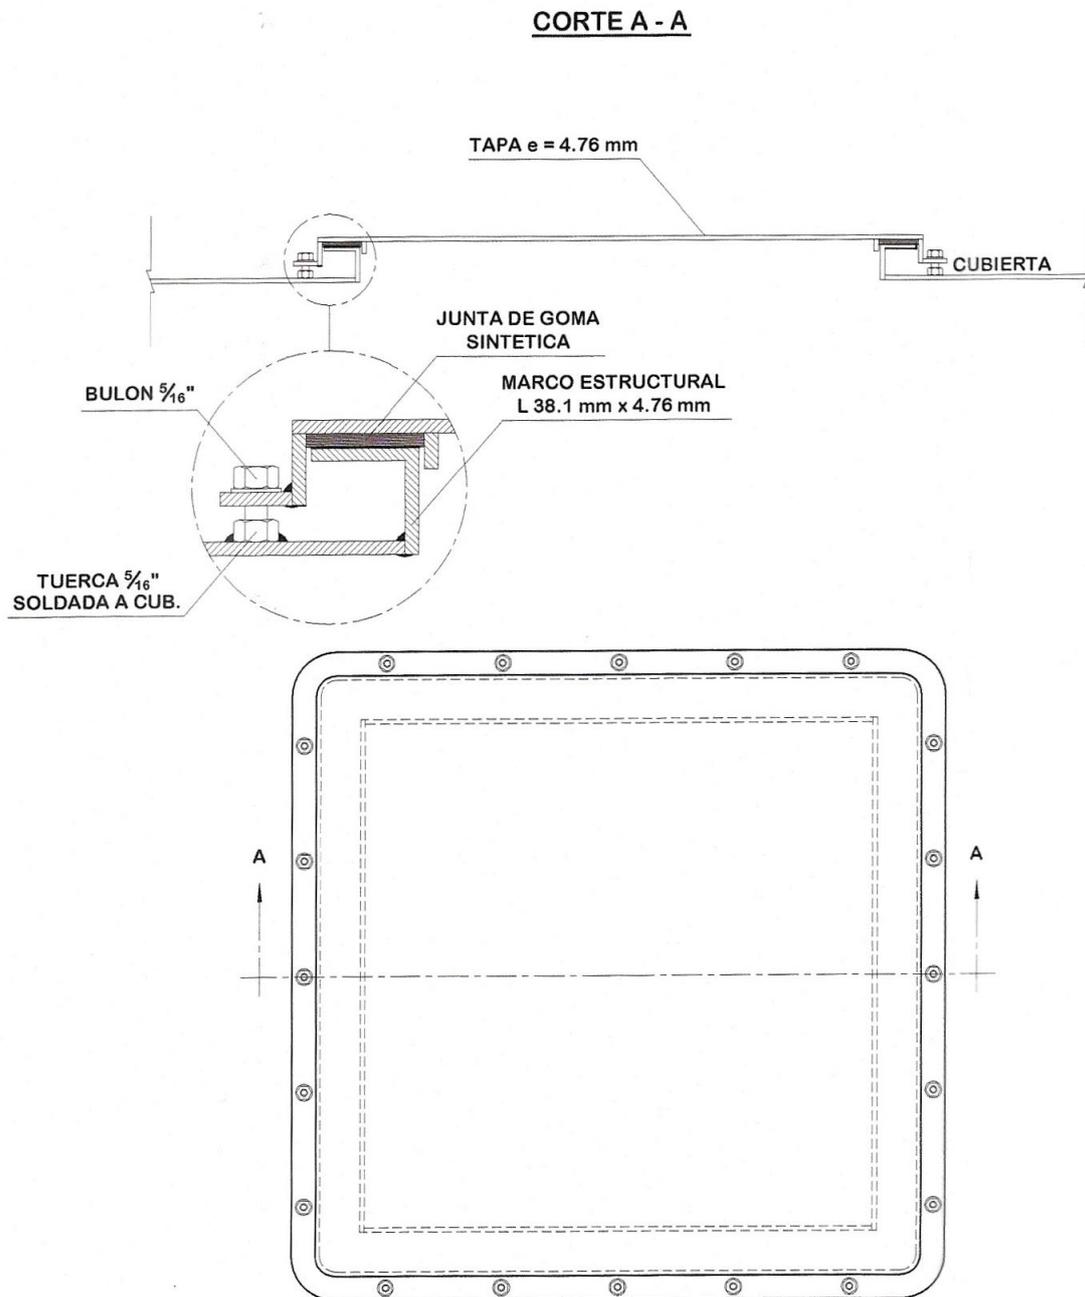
Detalles constructivos de la tapa de registro de acceso al tanque boyante.
